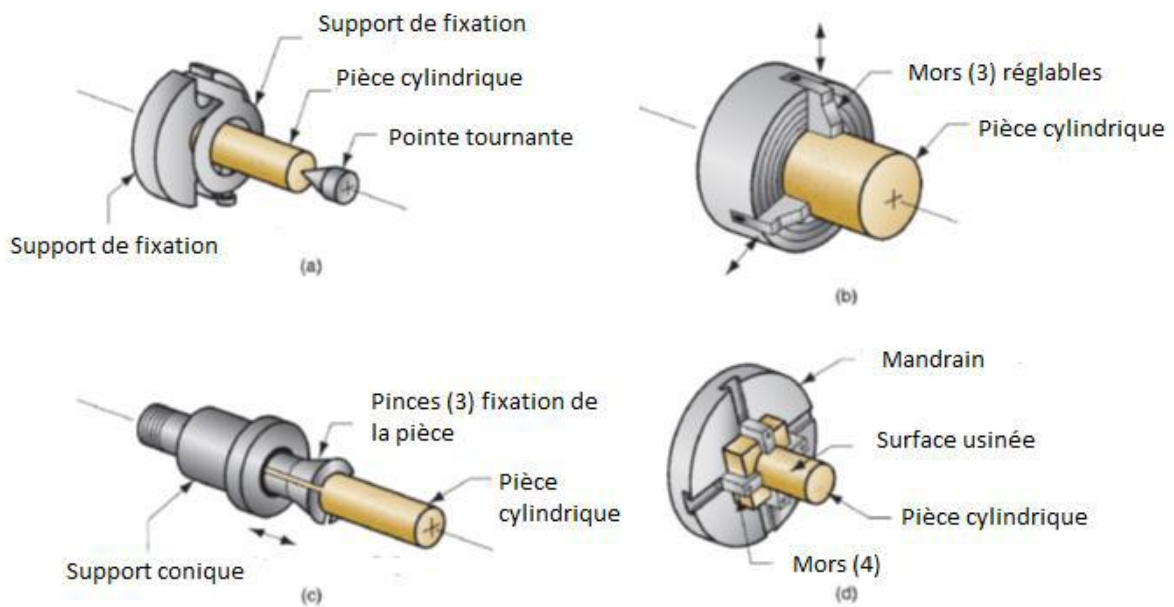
Quatre méthodes de serrage utilisées dans les tours: (a) montage de la pièce entre les pointes, (b) mandrin à trois mors, (c) pince de serrage et (d) plaque frontale pour les pièces à usiner non cylindriques.
